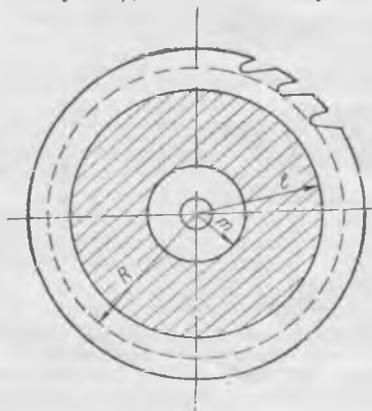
Схема расположения обрабатываемой зоны диска пилы
